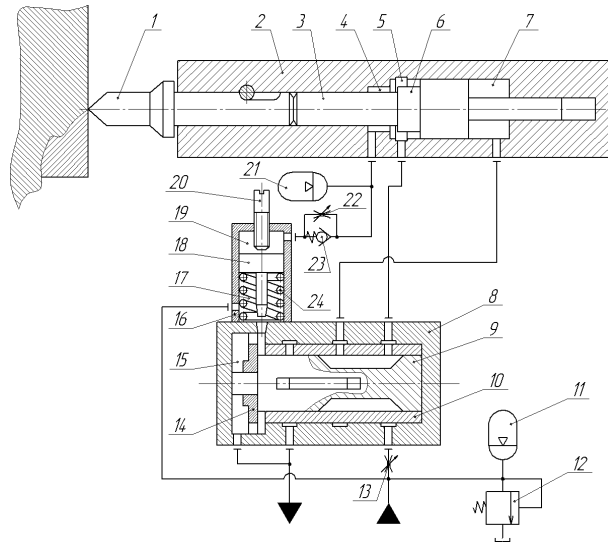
Схема гидравлического ударного устройства: 1 – инструмент; 2 – корпус; 3 – боек; 4, 5, 7 – камеры тормозная, обратного и рабочего хода; 6 – тормозная ступень бойка; 8 – распределитель; 9 – вращающийся золотник; 10 – неподвижная гильза; 11, 21 – гидропневмоаккумуляторы; 13 – регулируемый дроссель; 14 – турбина; 15 – камера распределителя; 16 – регулятор потока; 17 – дроссельная полость; 18 – поршень; 19 – поршневая полость регулятора потока; 20 – регулировочный винт; 22 – жиклер; 23 – обратный клапан; 24 – пружина
